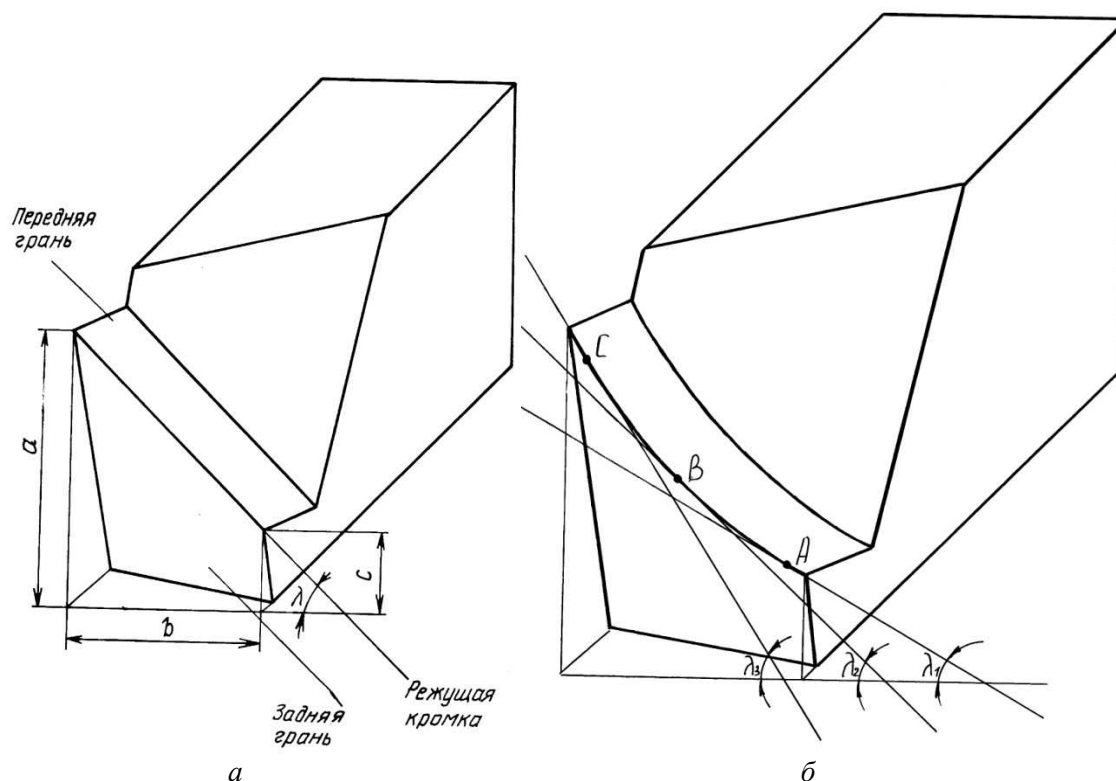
Конструкции безвершинных резцов: а – базовая конструкция; б – прогрессивная конструкция с регулируемым углом наклона кромки
